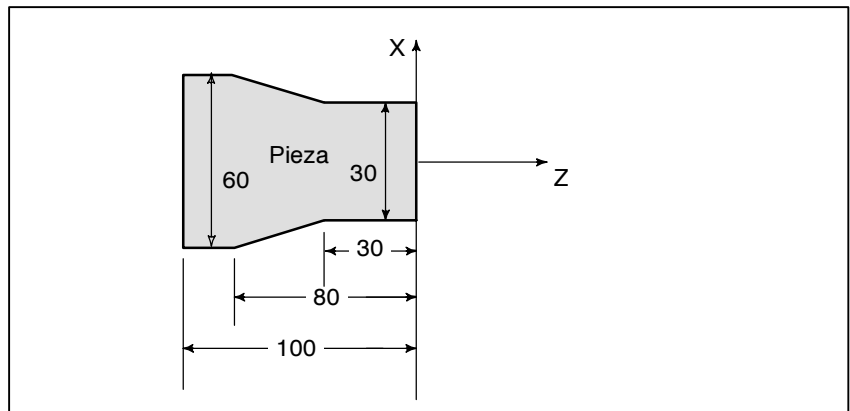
(e) Coordenadas y dimensiones en el plano de pieza
